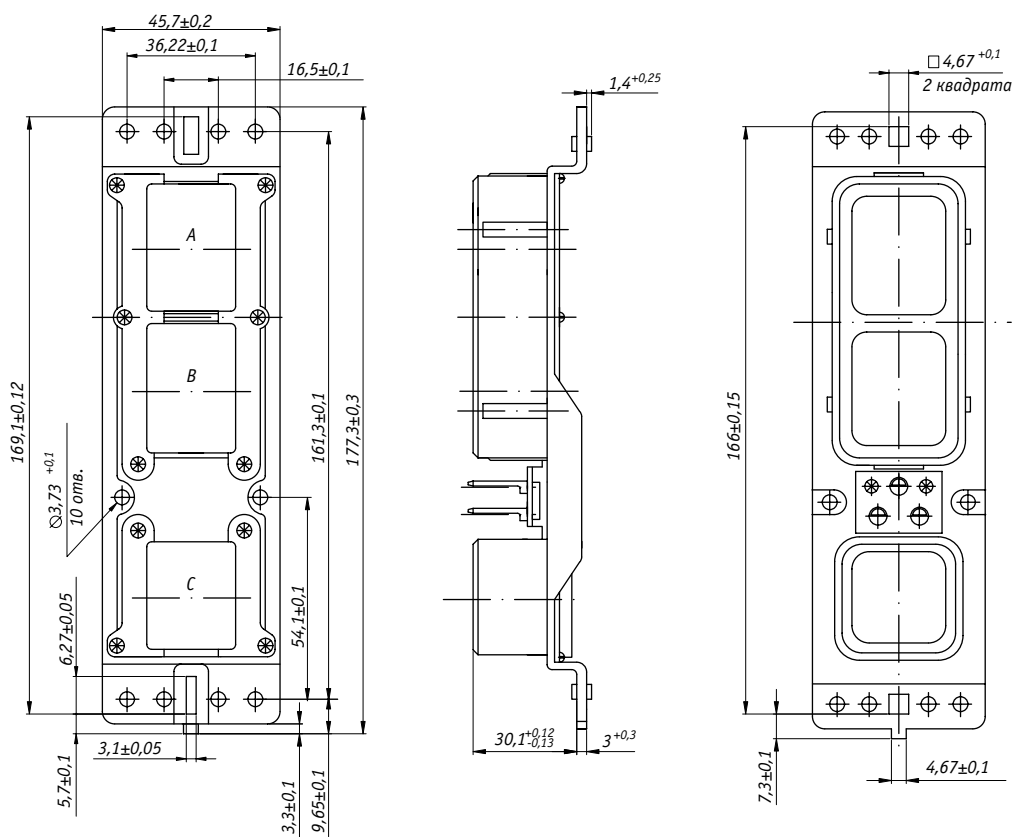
Корпус вилок 2 типоразмера для номеров схем расположения изоляторов в корпусе 201...232 (см. таблицу 3)
